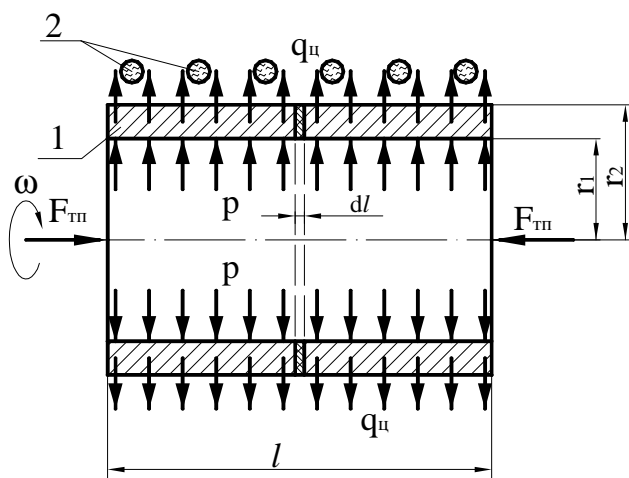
Схема термосилового нагружения цилиндрической оболочки (продольный разрез): 1 – цилиндрическая оболочка, 2 – индуктор.
